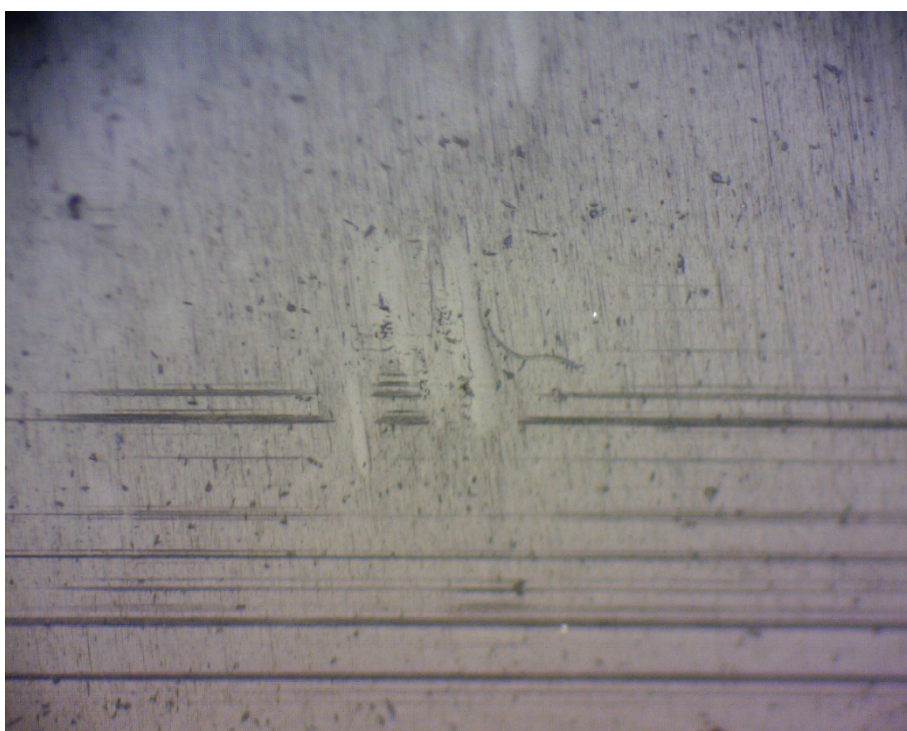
Impressão da superfície depois da aplicação no gearbox da turbina eólica nº 01-14
